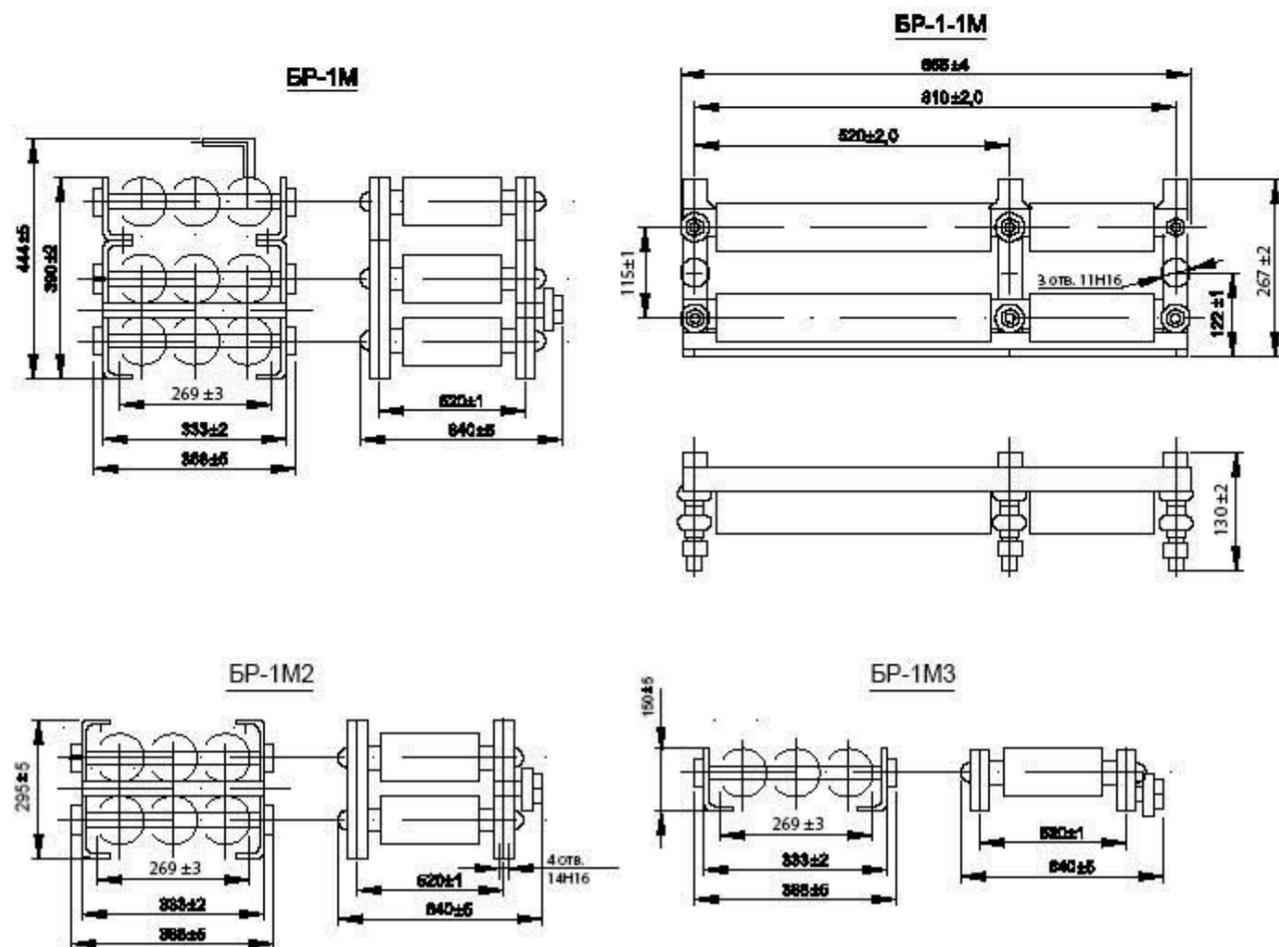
Габариты и установочные размеры блока резисторов типа БР-1М, БР-1М1, БР-1М2, БР-1М3 и БР-1-1М
